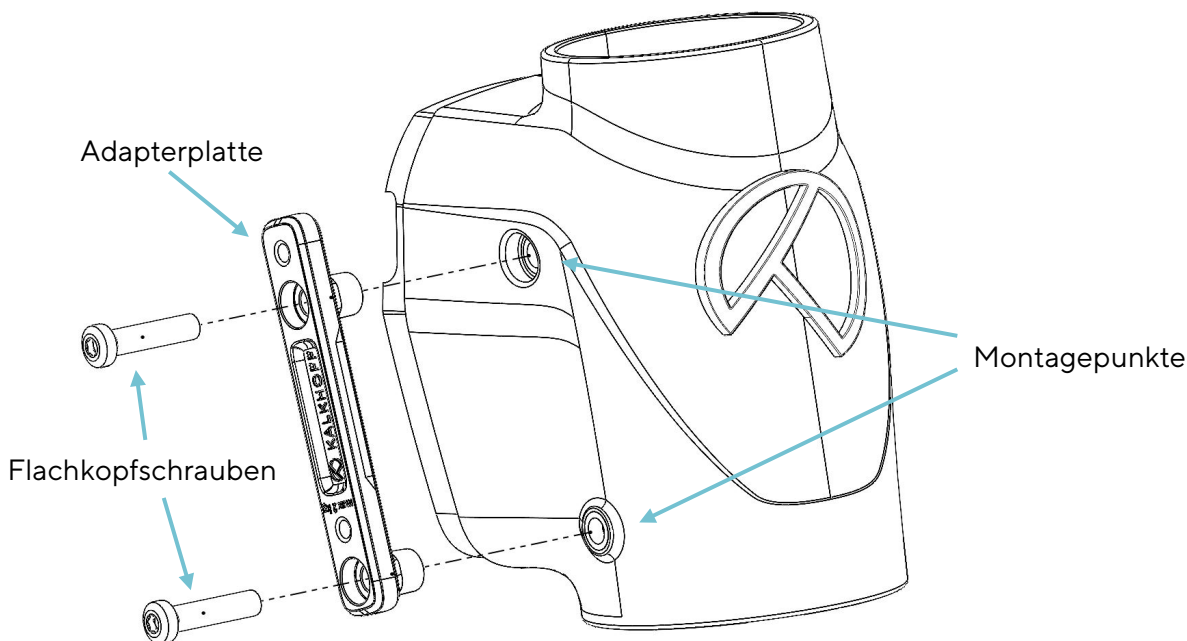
Flachkopfschrauben, Adapterplatte, Montagepunkte
